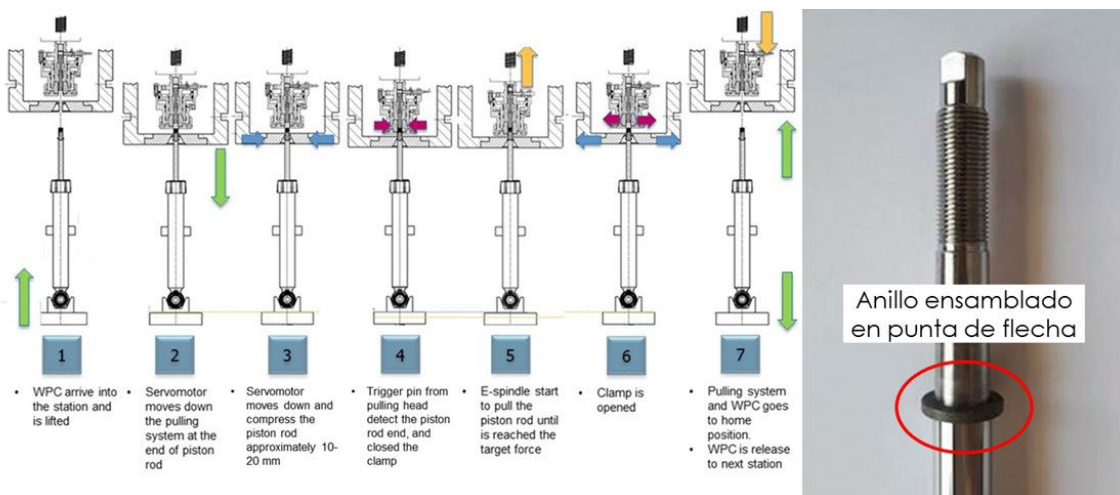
Esquema paso a paso del ensamble de anillo en flecha
